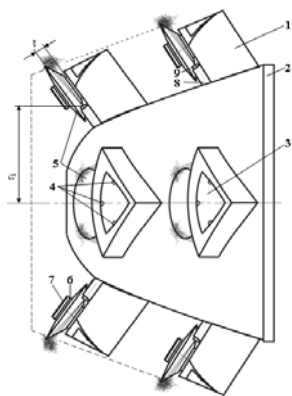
Общий вид реверсивной коронки с устройством пылеподавления
